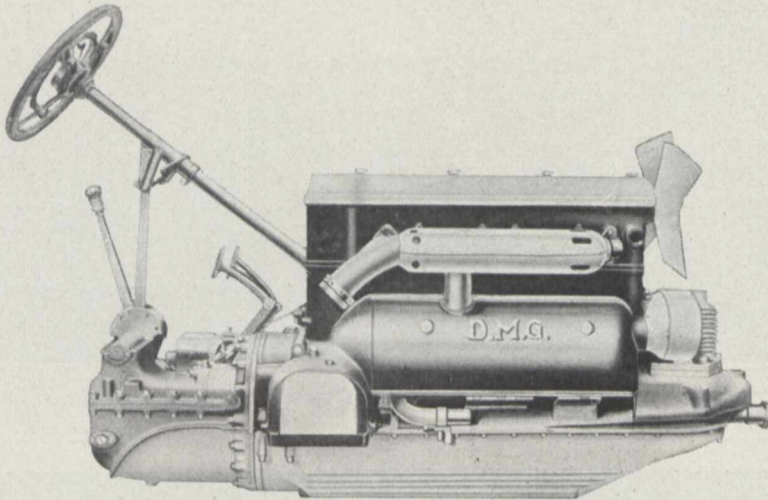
Motorgetriebeblock mit Kompressor vor den Zylindern.
